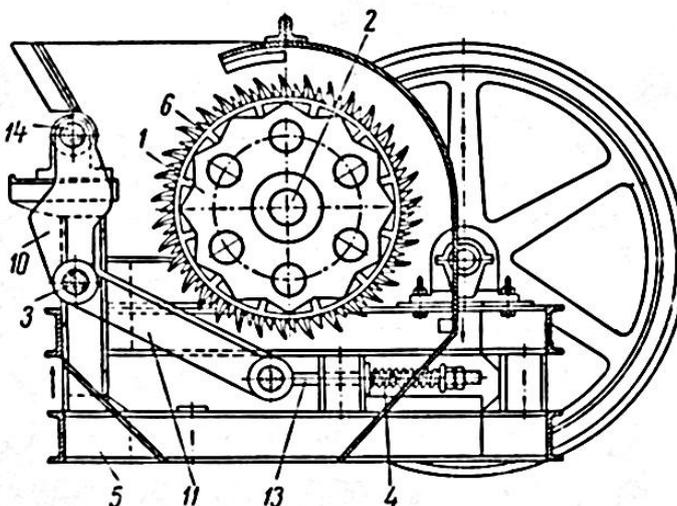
Одновалковая зубчатая дробилка: 1 – зубчатый валок; 2 – центральный вал; 3 – шарнирное крепление колосниковой решетки; 4 – пружина; 5 – станина; 6 – зубцы; 7 – приводной вал; 8 – колосники; 9 – зубчатая передача; 10, 11 – решетка; 12 – приводной шкив; 13 – тяга
